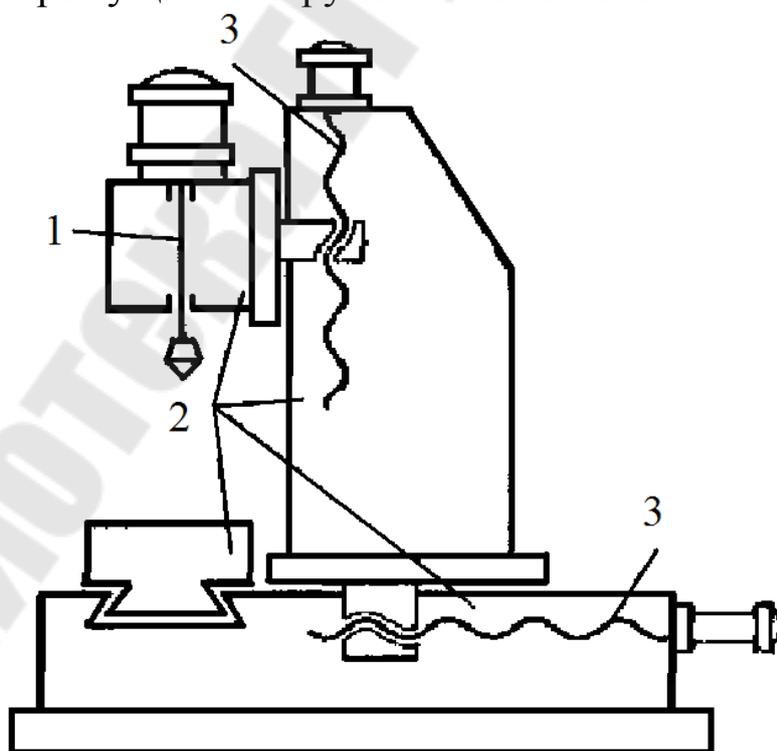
Основные узлы (сборочные единицы) металлорежущего станка: 1 – главный привод; 2 – базовые детали; 3 – приводы подачи
